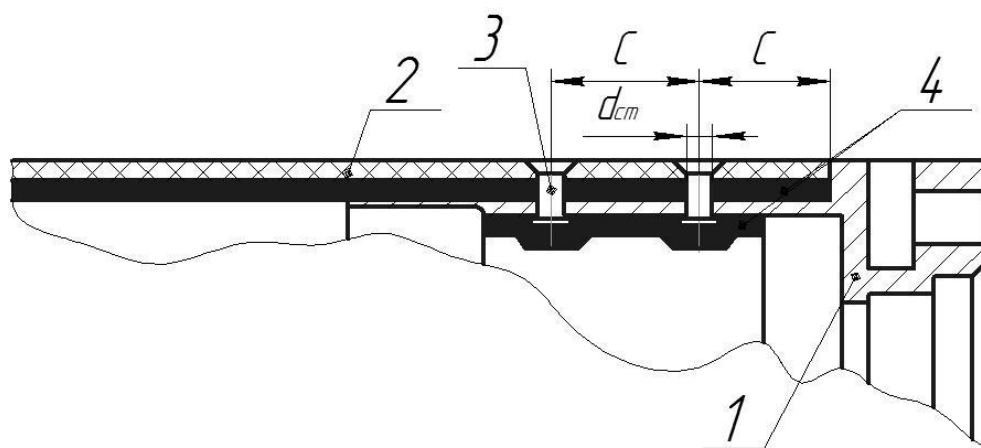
Комбіноване металопластикове з'єднання (поєднання клейового та заклепкового способів з'єднання): 1 – металевий каркас; 2 – оболонка з АКМ; 3 – заклепка; 4 – клей [44]
